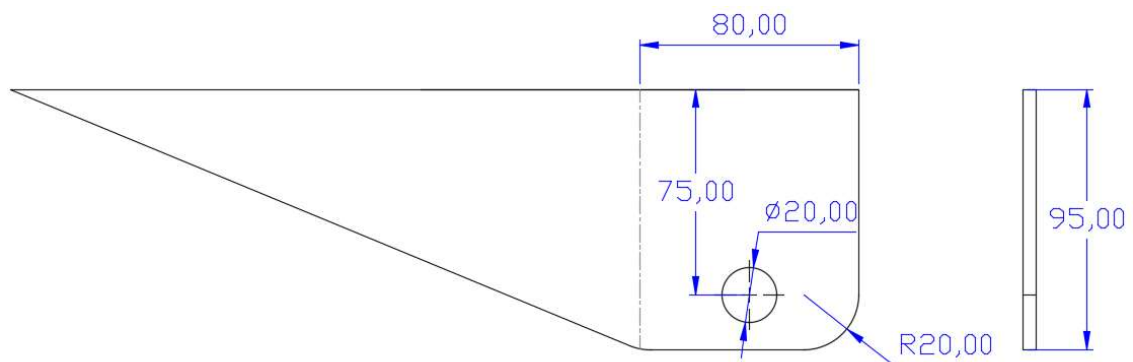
Dimensiones de la placa de unión pluma-actuador.
